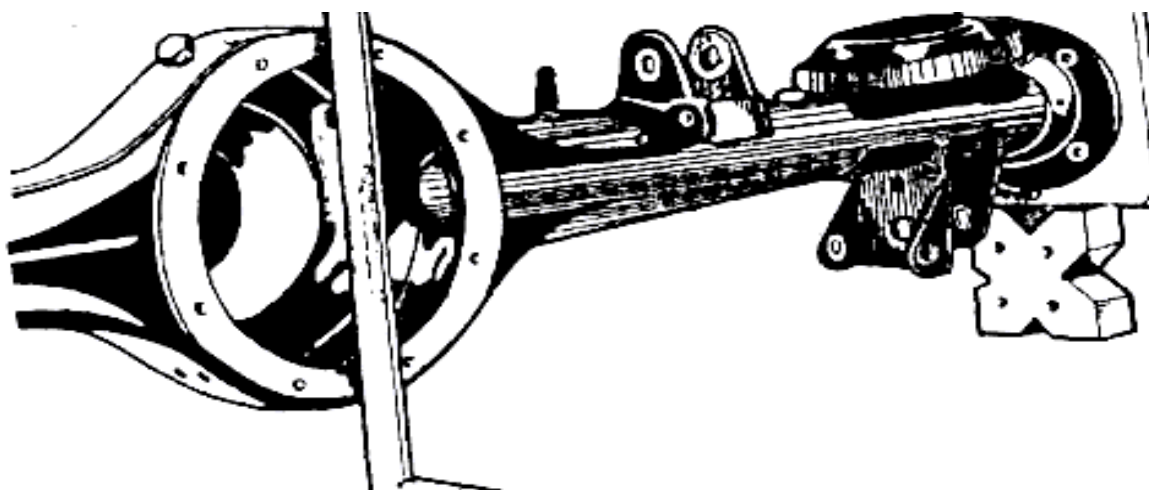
Проверка перпендикулярности поверхности крепления редуктора
